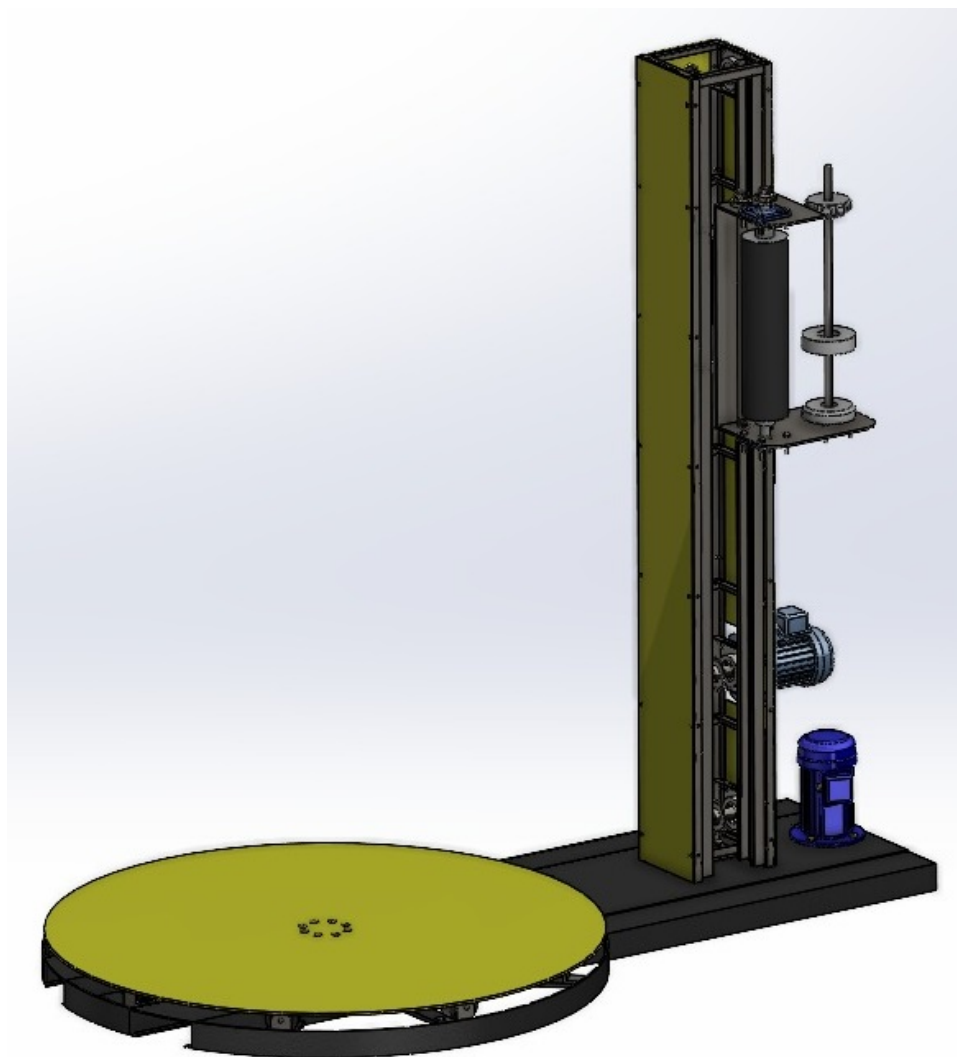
Máquina embaladora automática vertical diseñada en Soliworks.
